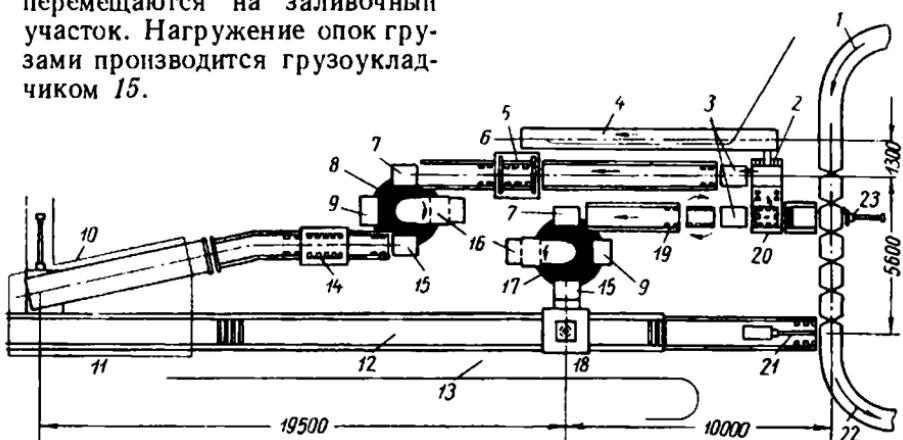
Схема автоматической линии изготовления форм для блоков цилиндров автомобильных двигателей:
